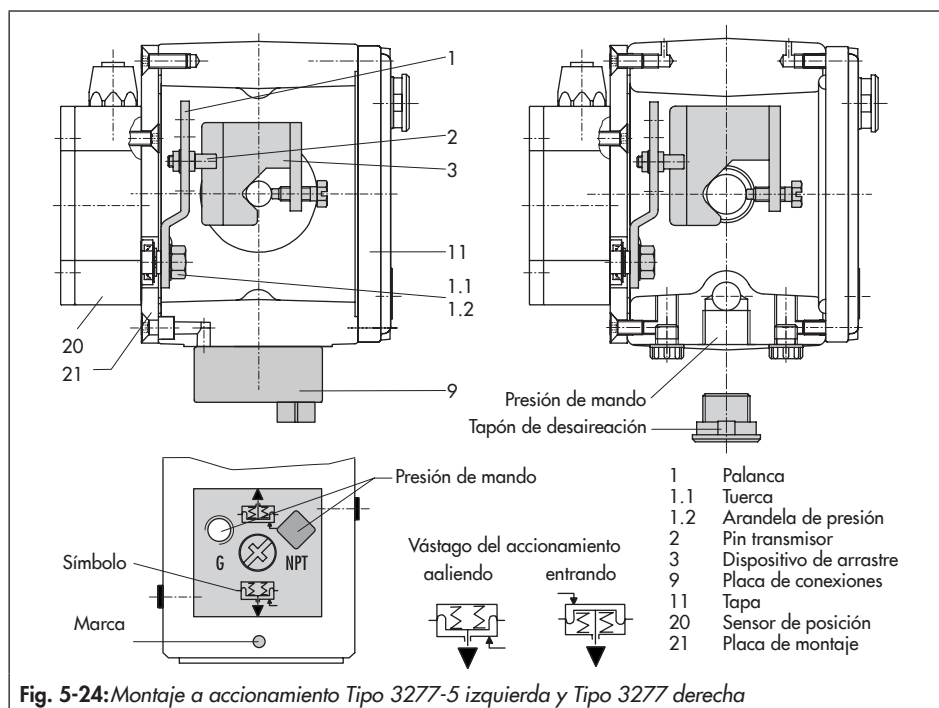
Montaje a accionamiento Tipo 3277-5 izquierda y Tipo 3277 derecha
